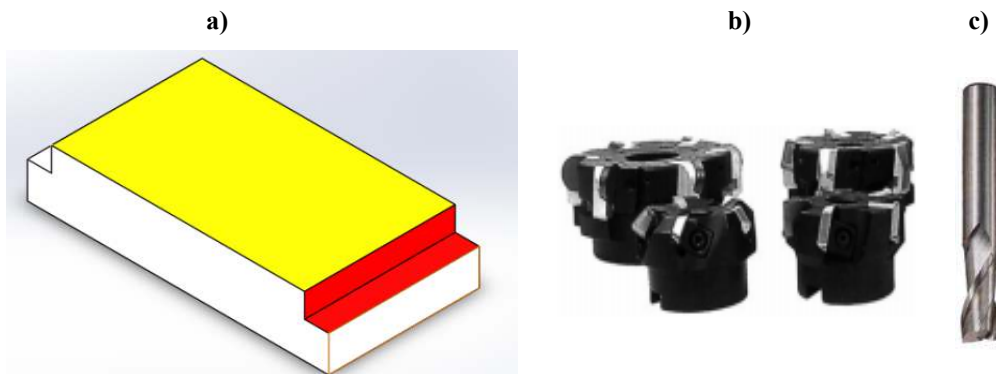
surfacage. a) usinage de la surface plane (couleur jaune) à l'aide d'une fraise à surfacer. Deux plans épaulés (surfaces rouges) réalisés par une fraise deux tailles, b) Fraise à surfacer, c) fraise deux tailles.
